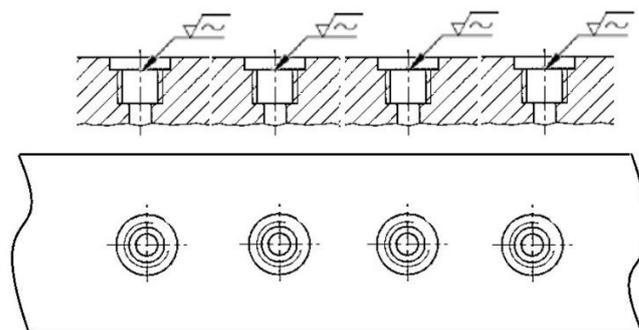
Planflächen bei Senkungen, Zeichnungsangabe
